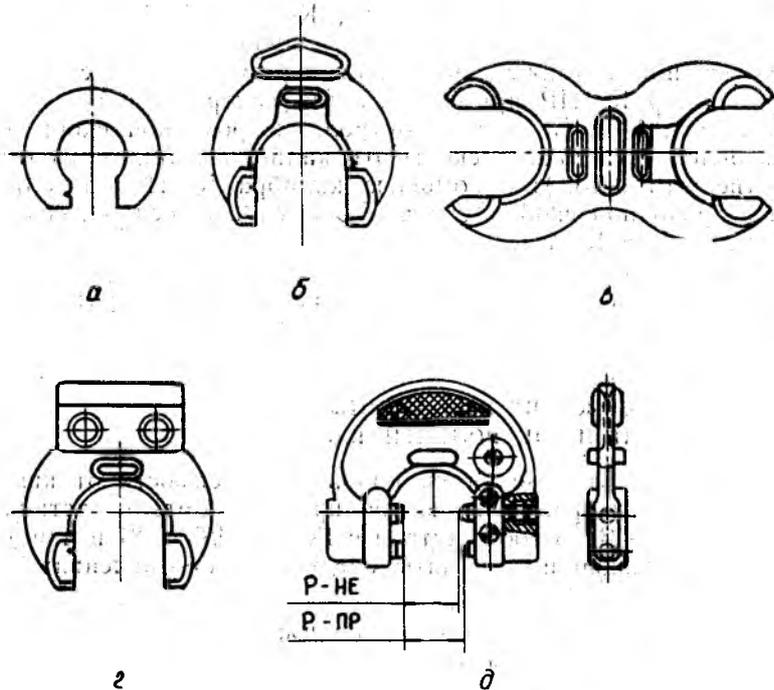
Основные типы калибр-скоб для контроля валов: а — скоба односторонняя ($D=1...180$ мм); б — скоба штампованная односторонняя $D=3...50$ мм); в — скоба штампованная двусторонняя ($D=3...100$ мм); г — скоба с ручкой штампованная односторонняя ($D=50...170$ мм); д — скоба односторонняя регулируемая (диапазон контролируемых размеров от 0 до 340 мм)
